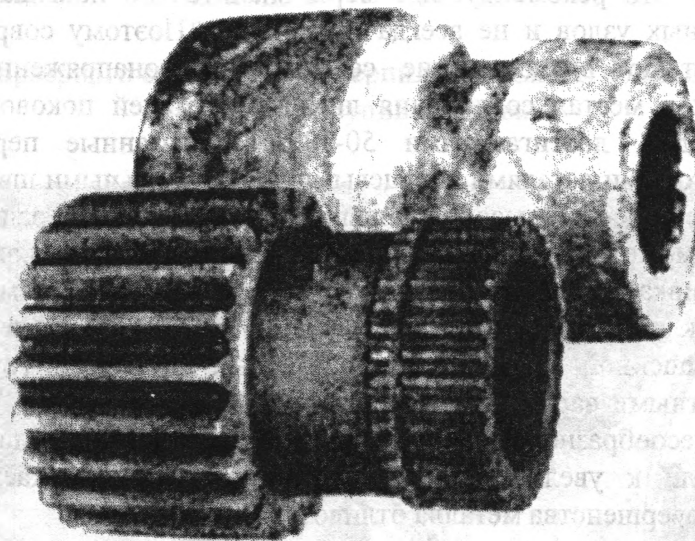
Крупногабаритное зубчатое колесо из литой недеформированной заготовки (вверху — заготовка; внизу — колесо)
